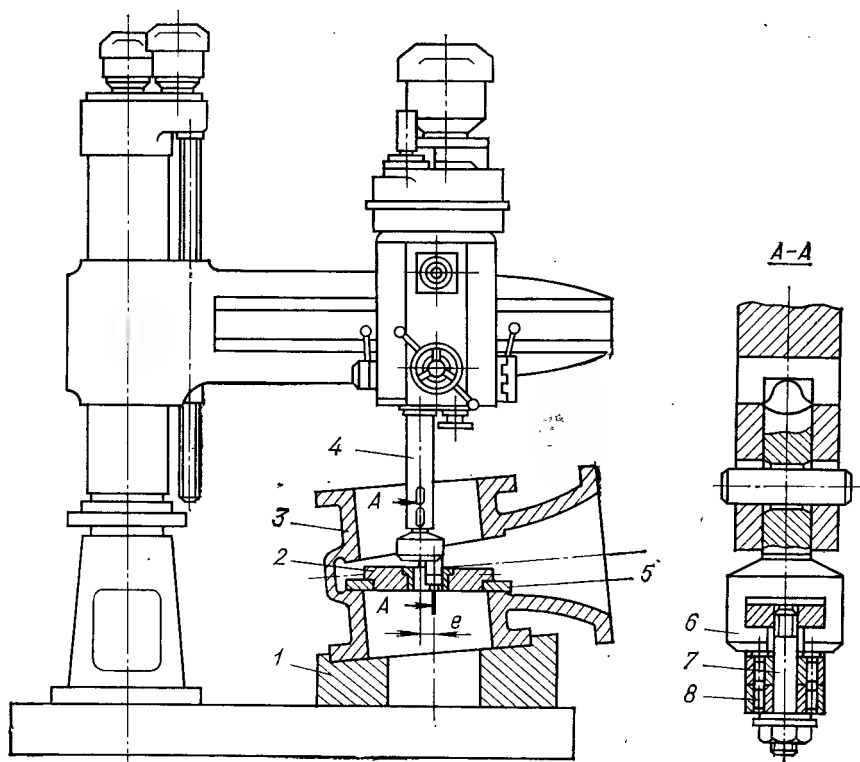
Притирка уплотнительных колец корпуса задвижки на радиально-сверлильном станке:
